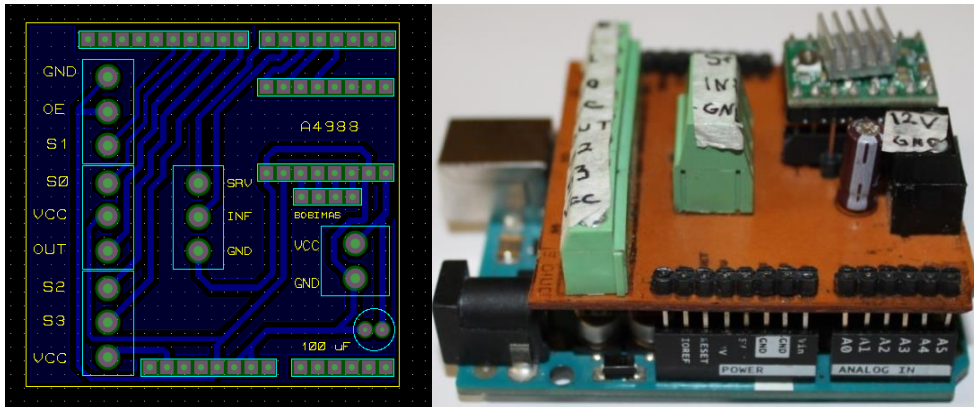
Diseño de la PCB y montaje sobre Arduino UNO.
